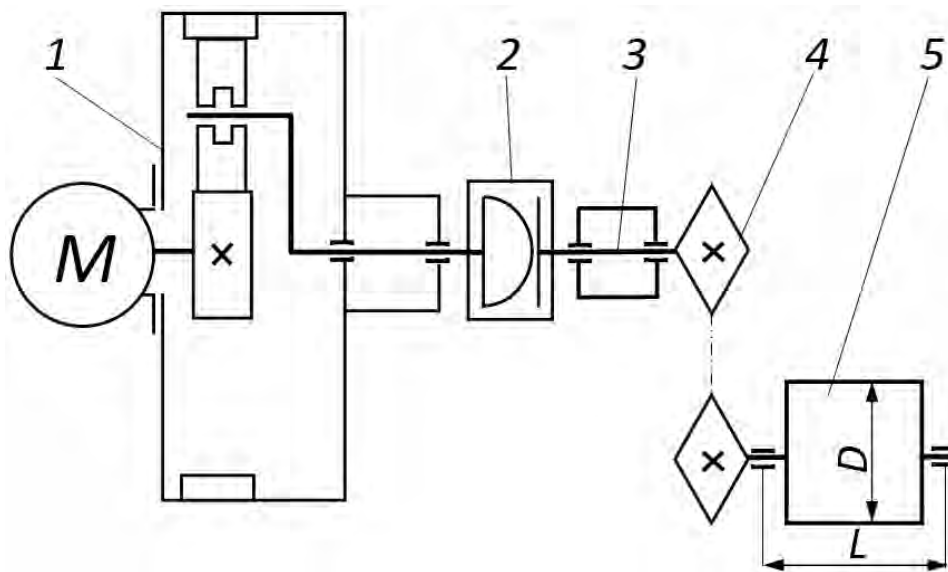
Схема привода тягового устройства (вид сверху): 1 – мотор-редуктор (асинхронный электродвигатель с фланцевым исполнением закреплен на корпусе планетарного редуктора); 2 – муфта кулачково-дисковая; 3 – промежуточный вал привода; 4 – цепная передача; 5 – приводной вал с барабаном
